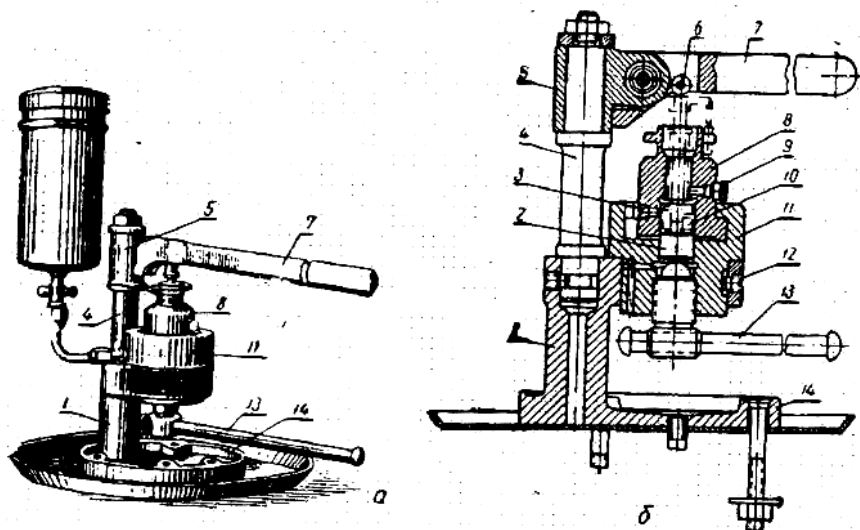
Прибор КИ-1640А для определения гидравлической плотности плунжерных пар: а – общий вид; б – продольный разрез; 1 – основание прибора; 2 – подпятник; 3 – винт-фиксатор гильзы плунжера насоса дизеля Д-108; 4 – стойка; 5 – втулка; 6 – ролик; 7 – рычаг; 8 – установочная головка; 9 – винт-фиксатор гильзы плунжера насоса 4ТН-8,5Х10; 10 – гильза плунжера; 11 – корпус прибора; 12 – нажимной винт; 13 – ворток; 14 – поддон
